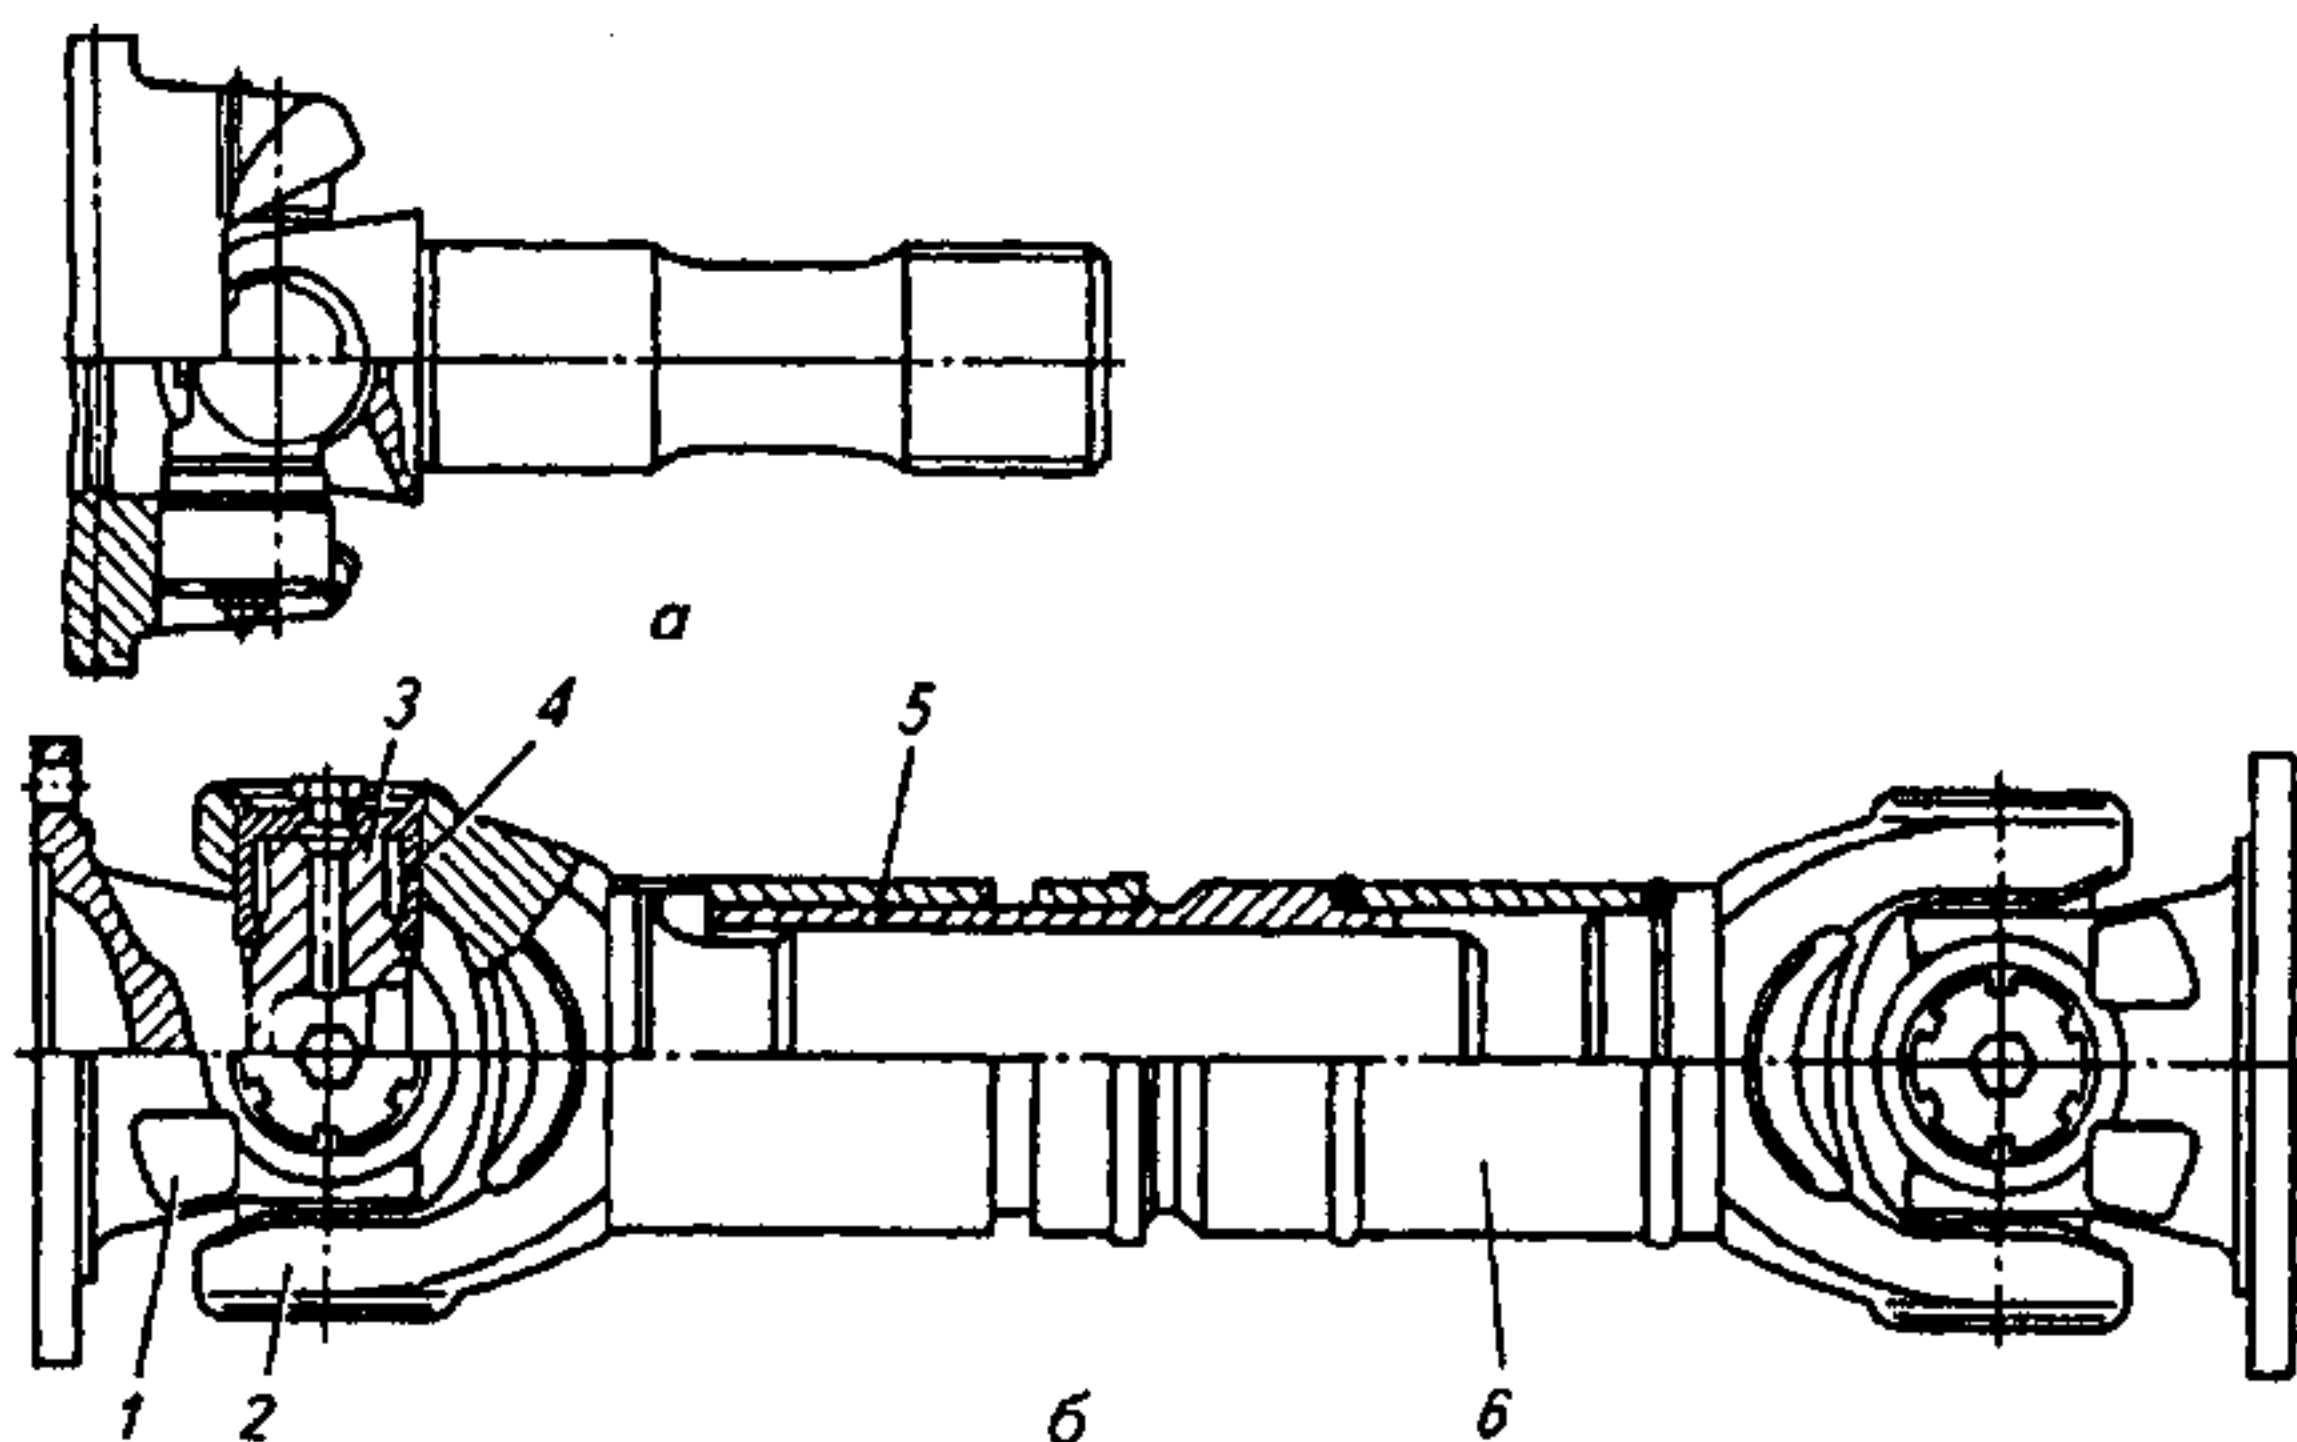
Карданные шарниры: а —простой; б— универсальный; 1 — ведущая вилка; 2—ведомая вилка; 3— крестовина; 4-игольчатый подшипник; 5— подвижное шлицевое соединение; 6 — труба карданного вала
